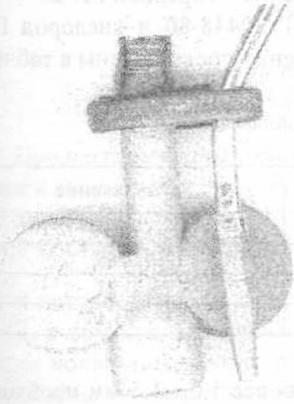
Газоструйный излучатель, смонтированный на газопламенной горелке
